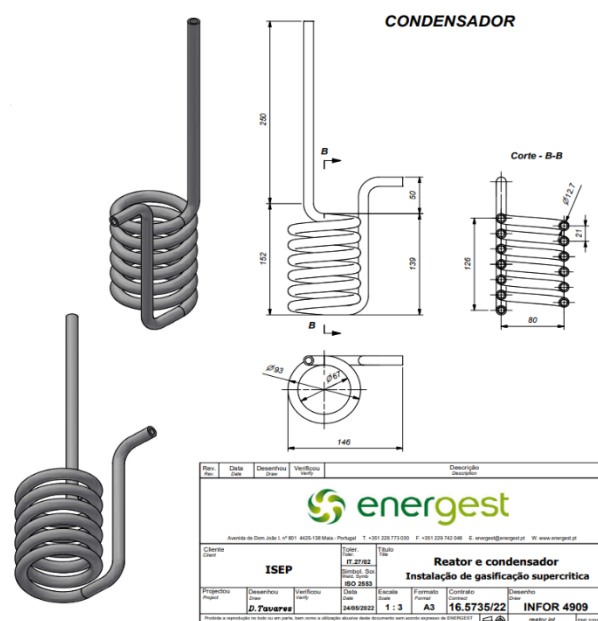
Desenho técnico da serpentina integrada no sistema de condensação.
